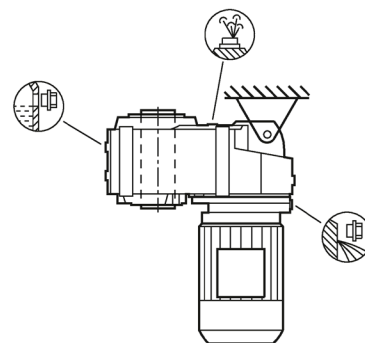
Einbaulagen für Flachgetriebe F.AD Aufsteckausführung Baugröße 29
